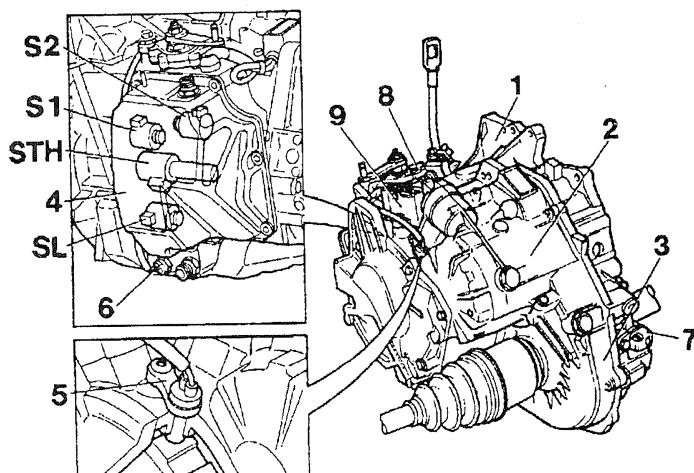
Aisin AW 50-42. Автоматическая коробка передач (1 – кожух; 2 – корпус; 3 – корпус главной передачи заднего моста; 4 – кожух клапанной коробки; 5 – датчик числа оборотов; 6 – датчик температуры, 7 – датчик спидометра; 8 – датчик положения переключения передачи; 9 – контактный элемент).
